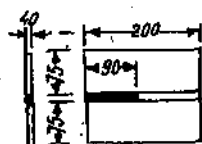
Брус, сваренный до половины длины шва, подготовленный для наблюдения за магнитным полем.
